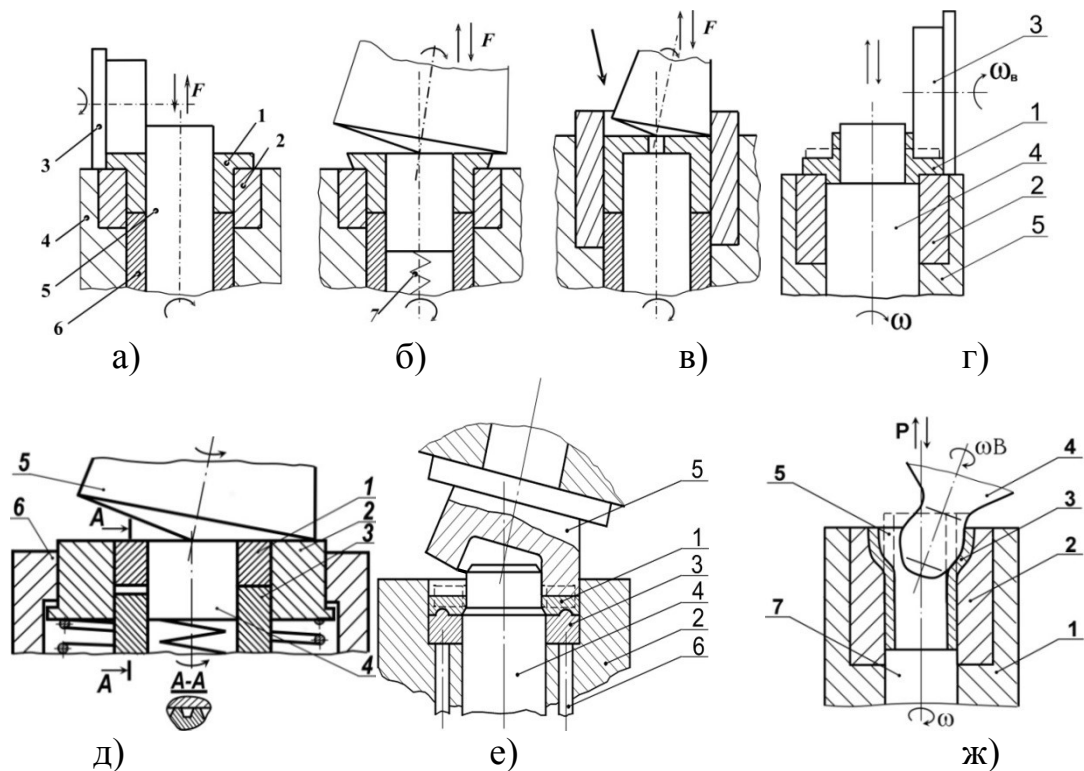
Схеми торцевого розкочування циліндричним і конічним валками: висаджування зовнішнього бурта (а), (б); висаджування внутрішнього бурта (в); висаджування і зворотне витискування (г); пряме витискування зубчастої поверхні (д); осаджування-калібрування (е); роздавання-калібрування (ж)
